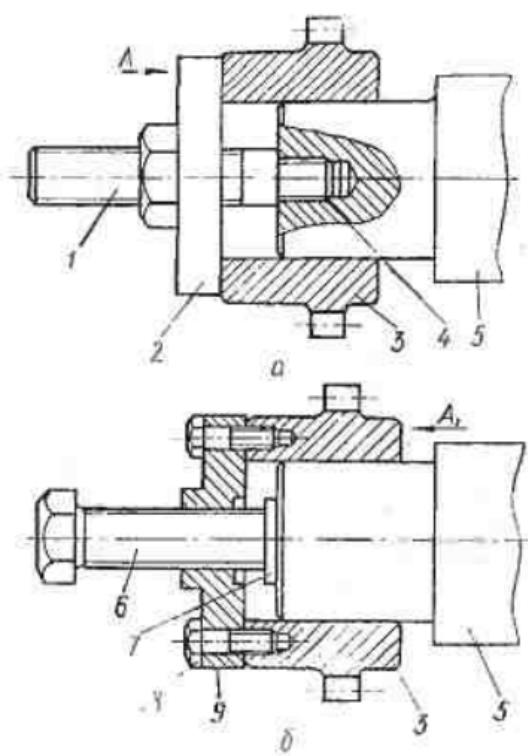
Схема напрессовки (а) и спрессовки (б) полуумфты:
